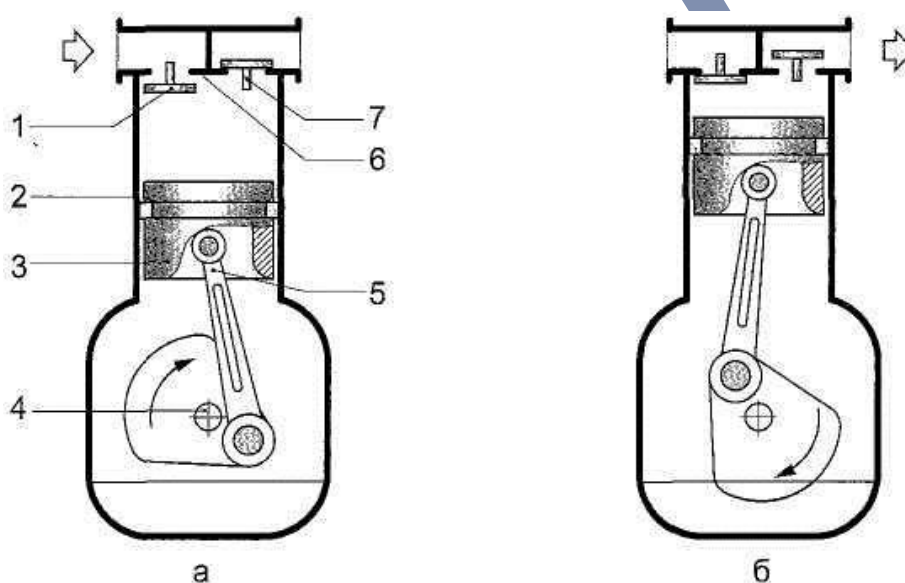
Поршневий компресор простої дії: а – зворотний хід; б – прямий хід; 1 – всмоктувальний клапан; 2 – циліндр; 3 – поршень; 4 – приводний вал; 5 – кривошипно-шатунний механізм; 6 – клапанна кришка; 7 – нагнітальний клапан [5].
